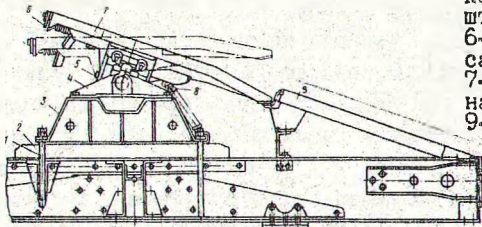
Тяговый прибор: 1-защитный кожух; 2-шплинт; 3-гайка; 4-кожух; 5-поджимная пластинка; 6-упругий элемент; 7-буксирный крюк; 8-крышка; 9-ось.
